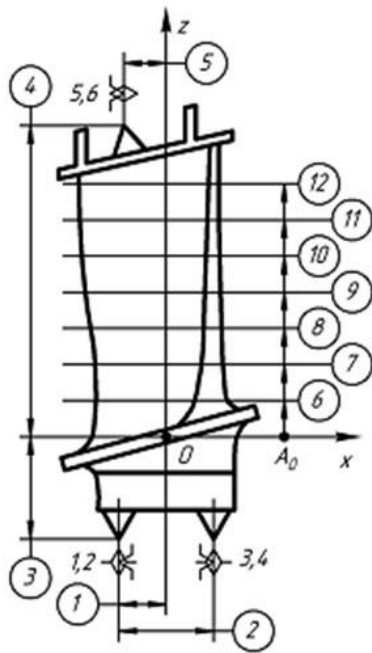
схема заготовки (відливки) лопатки турбіни з виконаними на ній технологічними базами для механічної обробки, які закоординовані з проточною частиною лопатки.
